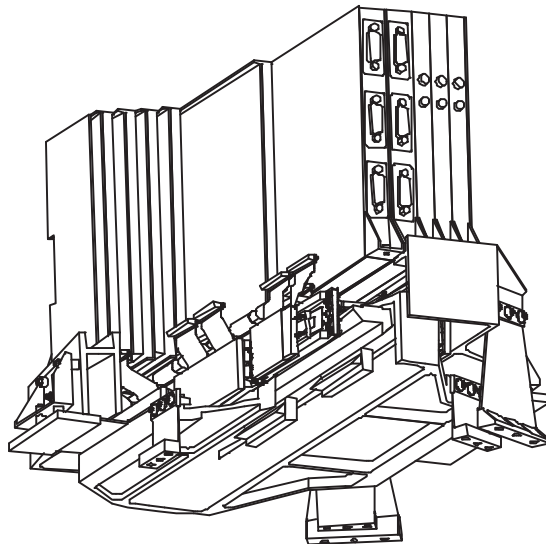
Vue du Sous-Ensemble de Détection Hautement Intégré (SEDHI)
